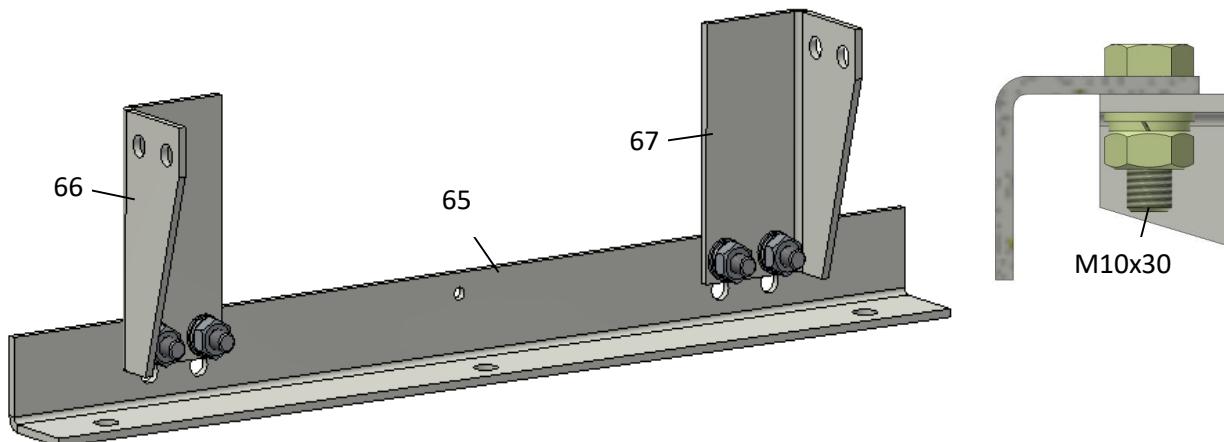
Сборка узла под верхние опорные изоляторы для ВЭ с ВМПЭ-10 или ВМПП-10
